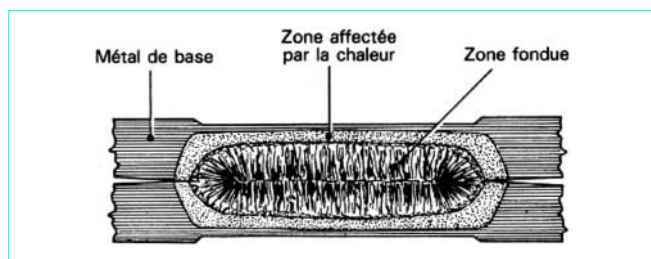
Soudage par points : coupe d'un point de soudure
